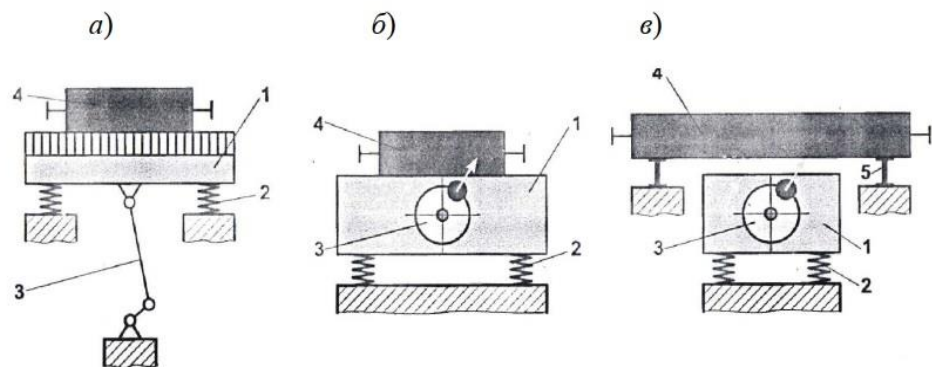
Схеми типових вибивних решіток: а – ексцентрікова; б – інерційна; в – ударна інерційна; 1 – решітка; 2 – опорні пружини; 3 – механічний привід; 4 – ливарна форма; 5 – опорна рама
